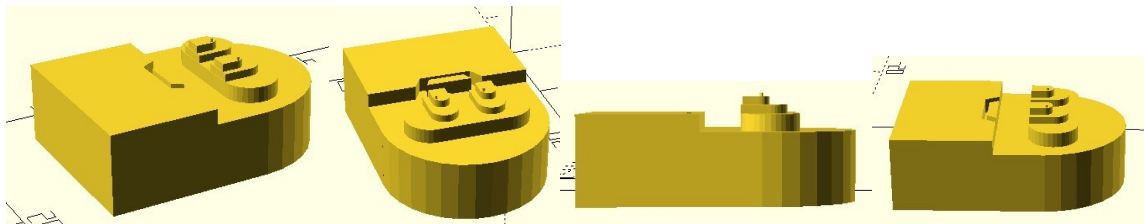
Obrys očí, Obr. 29 – Pozadí očí, Obr. 30 – Odlesk, Obr. 31 – Panenky, Obr. 32 – Otvor pro ústa, Obr. 33 – Ústa
